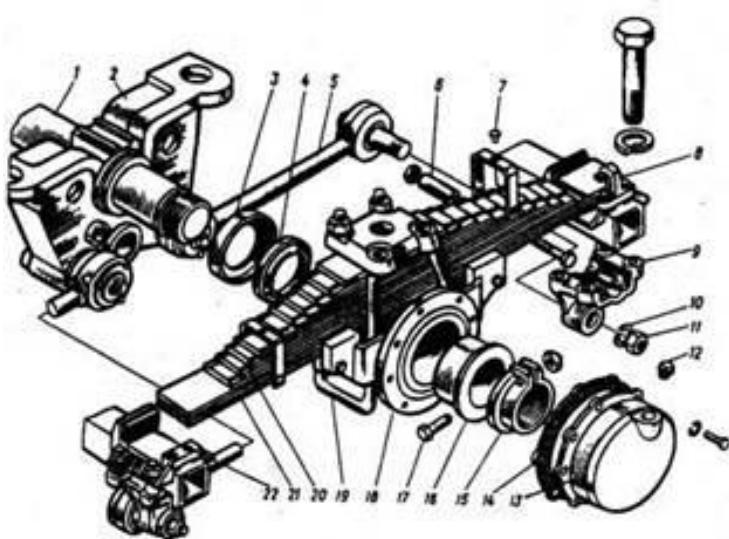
Задняя подвеска автомобилей КамАЗ-53212, -54112 и -5511: 1 - ось; 2 - кронштейн оси балансира; 3 - уплотнитель нос кольцо башмака рессоры; 4 - манжета; 5 - реактивная штанга; 6 - распорная втулка; 7 - заклепка; 8 - ограничитель качания мостов; 9 - нижний реактивный рычаг; 10 - пружинная шайба; 11 - гайка; 12 - пробка; 13 - крышка башмака; 14 - прокладка крышки; 15 - гайка крепления башмака; 16 - втулка башмака; 17 - болт; 18 - башмак рессоры; 19 - стремянка рессоры; 20 - лист; 21 - лист; 22 - передняя опора рессоры
